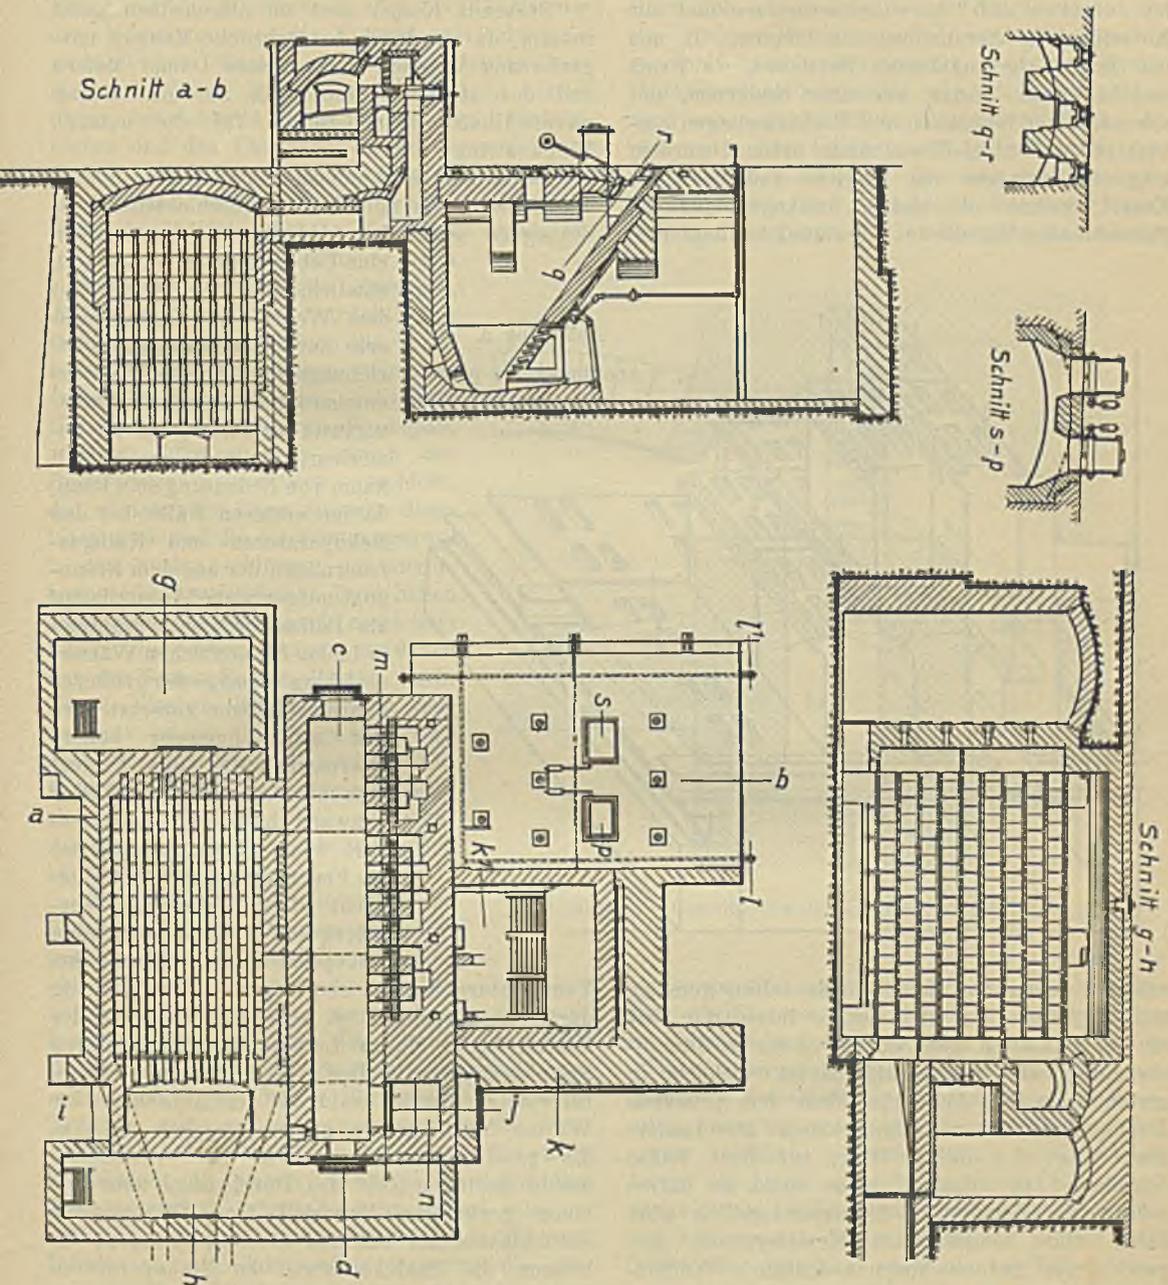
Rekuperator-Röhrenschweißofen.
